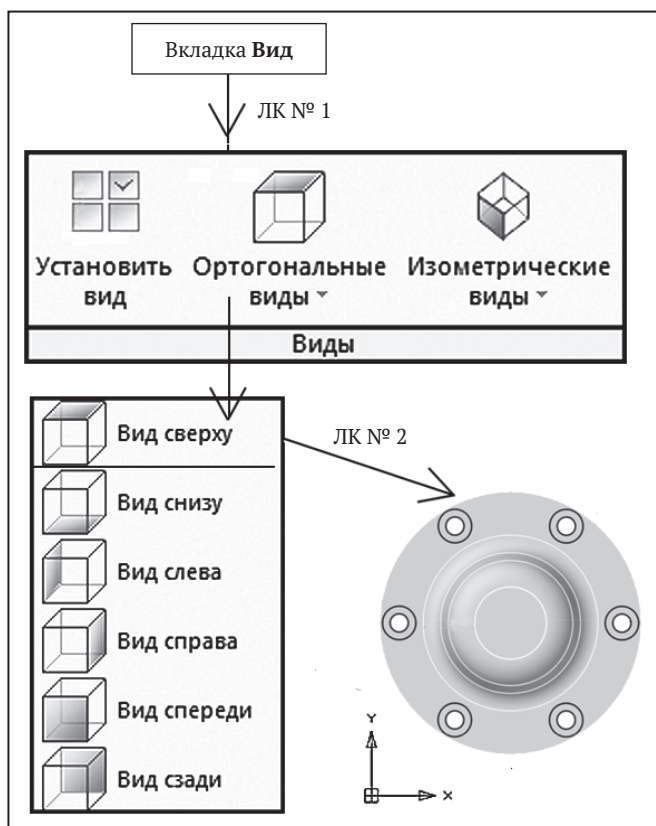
Способ № 3. Схема образования Виду сверху 3D-модели детали «Крышка» (визуальный стиль Реалистичный)
